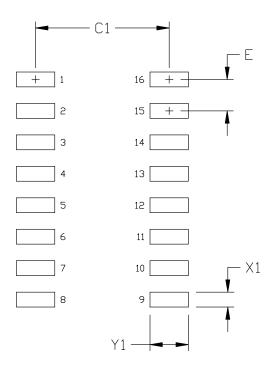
SOIC16 PCB 焊盘布局图
